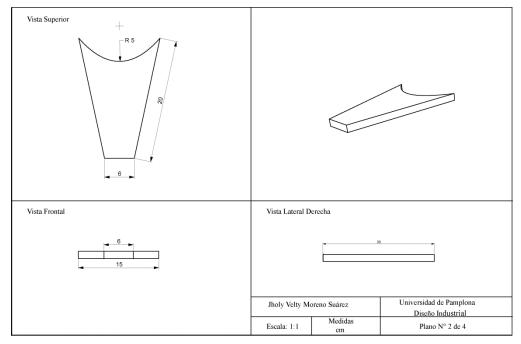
Plano 2 Carga todo. Fuente: Autor
